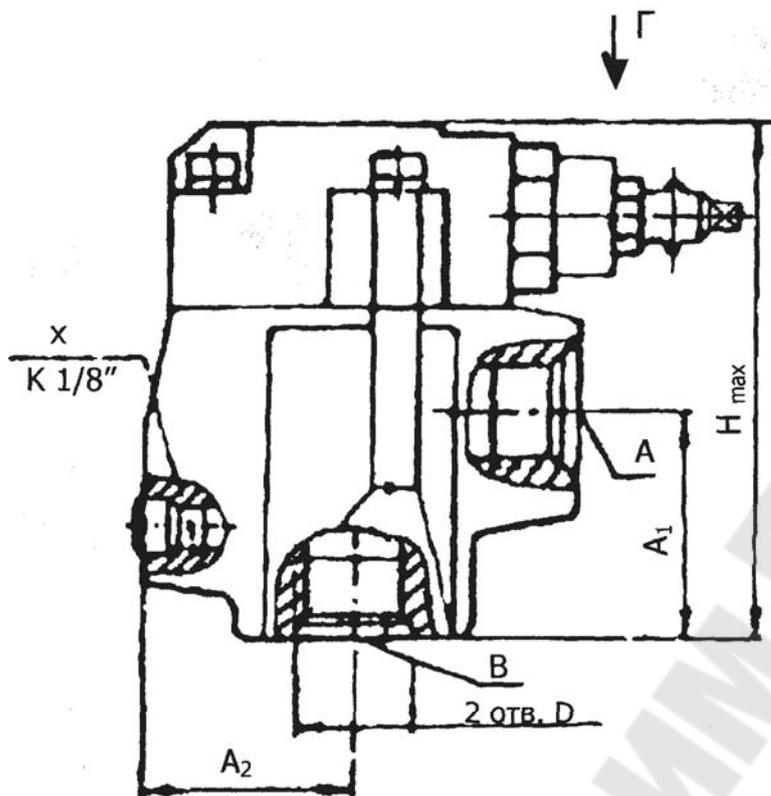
Общий вид и присоединительные размеры клапанов редукционных МКРВ - */3С
